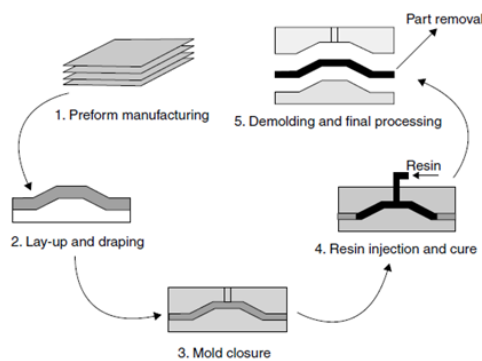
Procédé RTM pour la fabrication des pièces composites.
